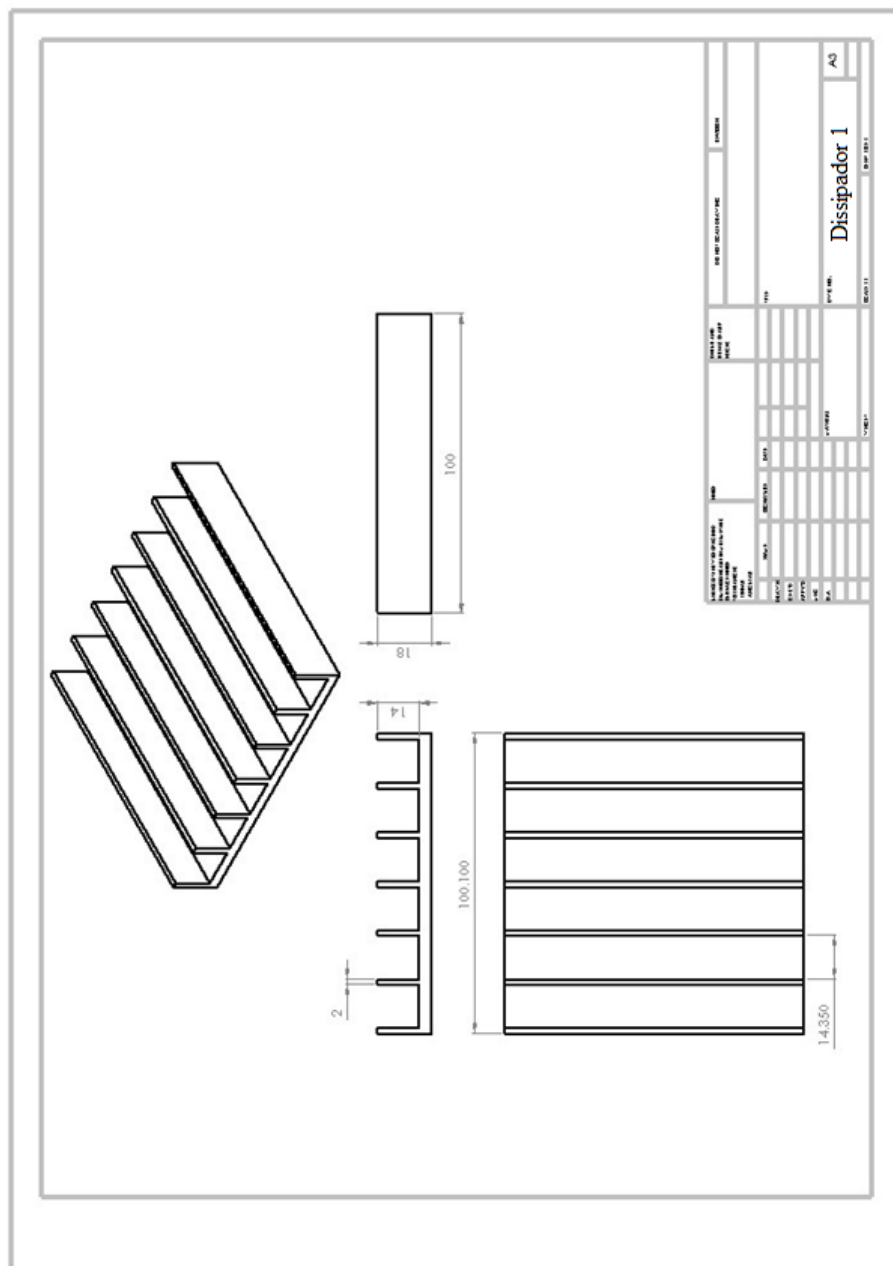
Desenho técnico utilizado para confecção do Dissipador 1.
